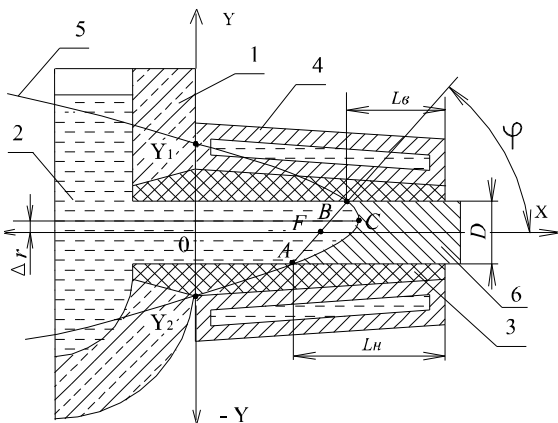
Схема расположения фронта затвердевания в вертикальной плоскости, проходящей через ось заготовки:
